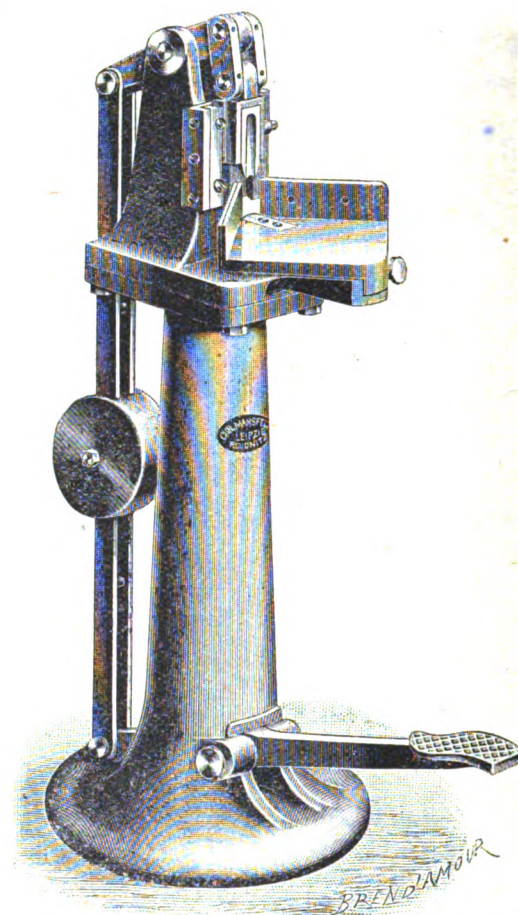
Eckenrundstoßmaschine von Fritz Huck, Krefeld.
